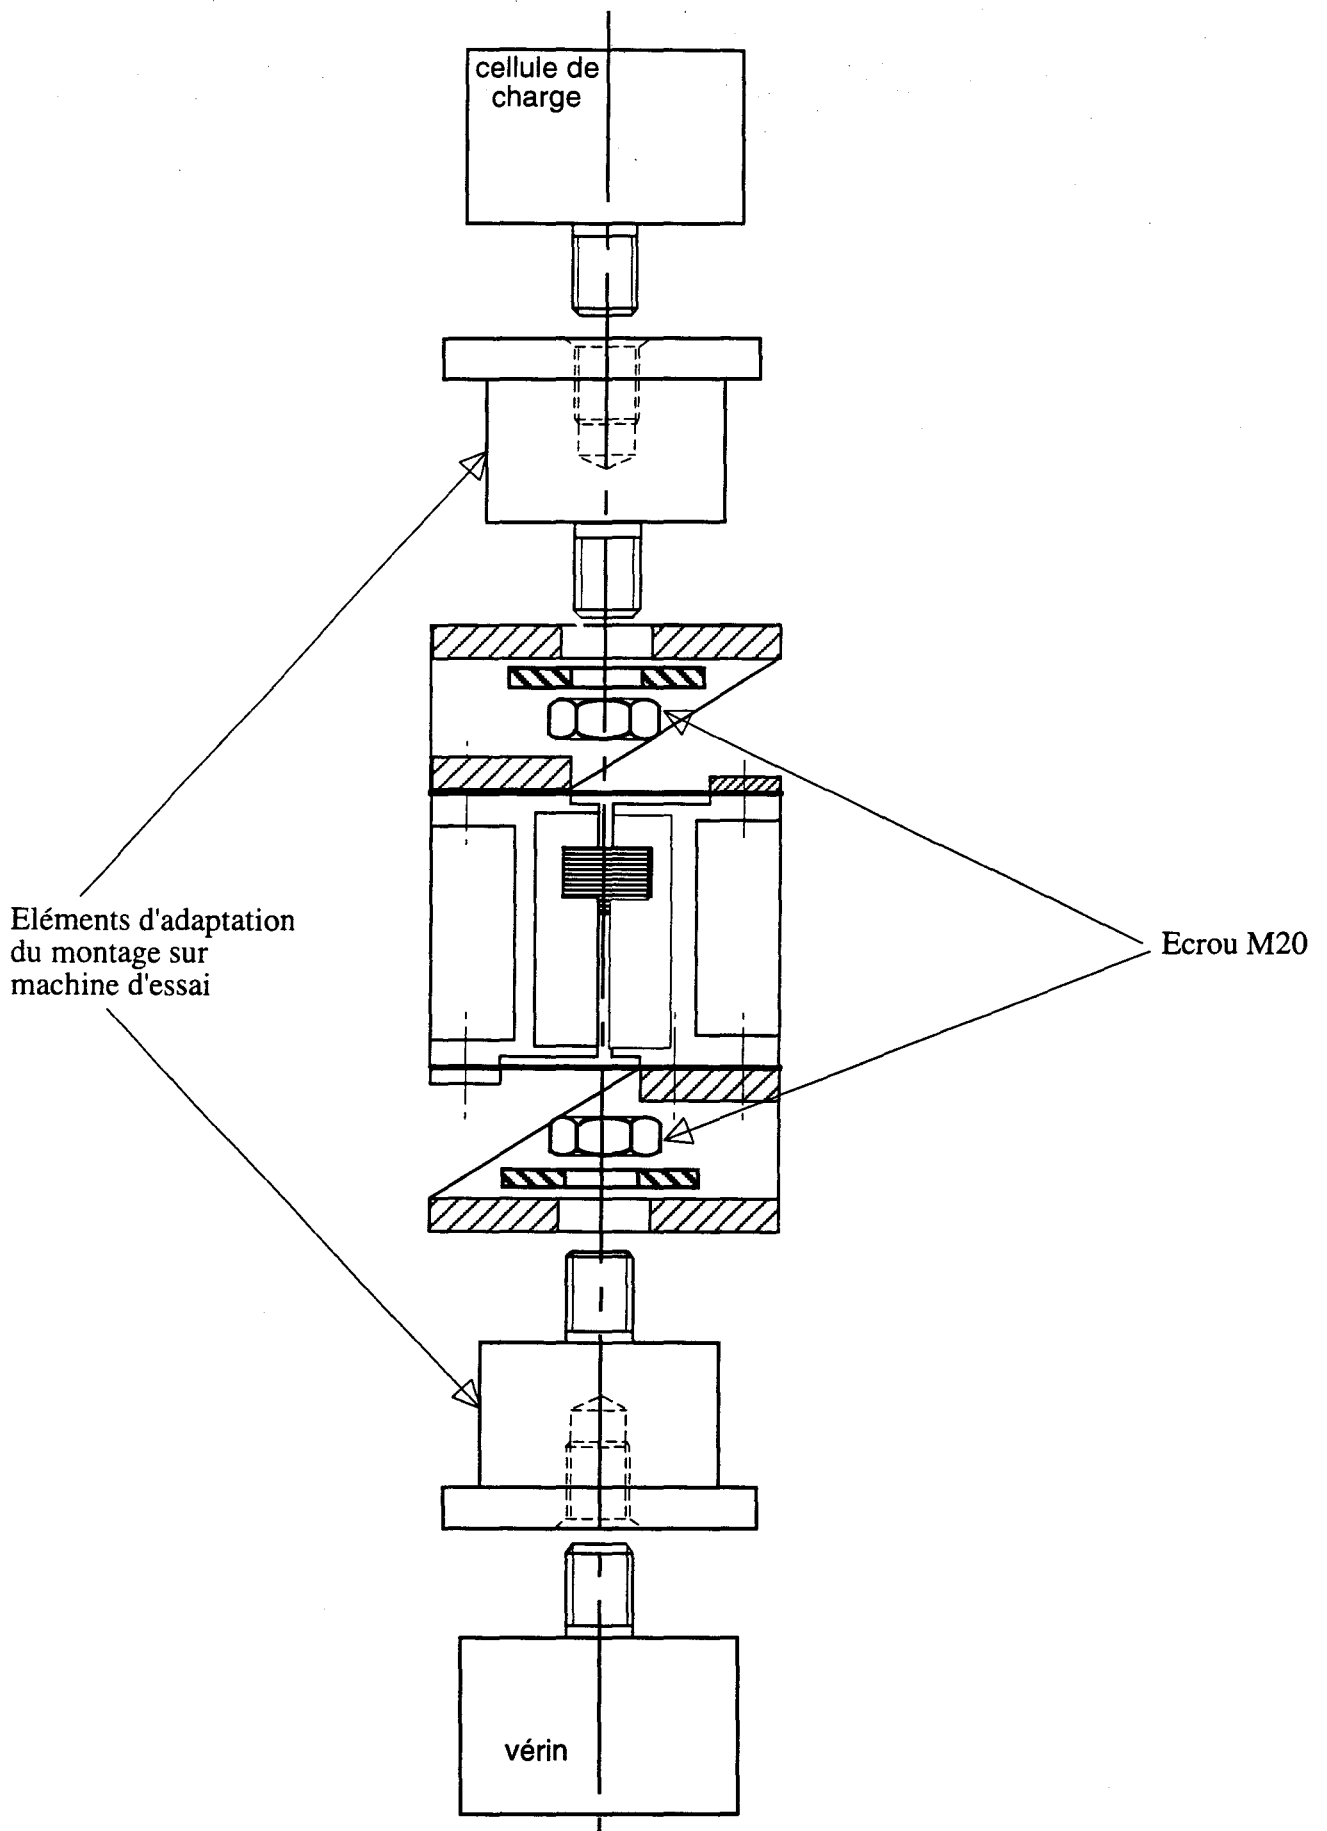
pièces d'adaptation du la montage sur machine d'essai INSTRON (EC Lille)
